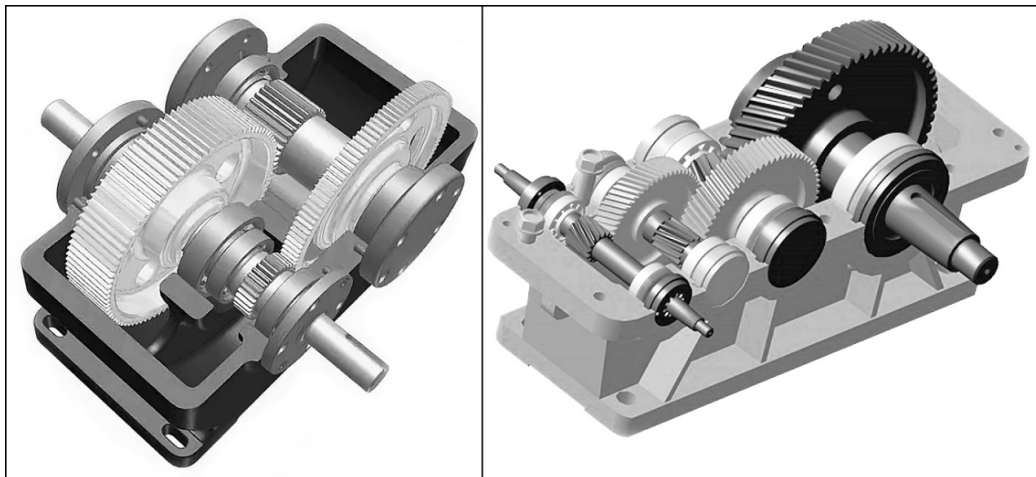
Примеры редукторов с прямозубыми и косозубыми зубчатыми колесами
